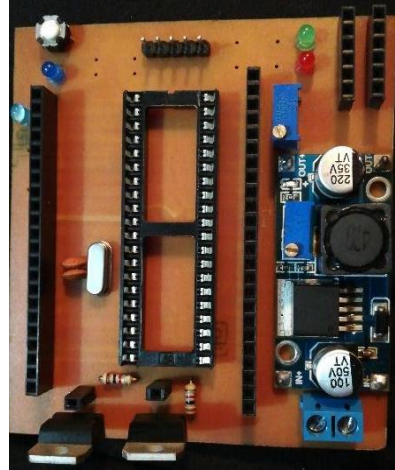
Baquela ruteada y componentes soldados (elaboración propia)
